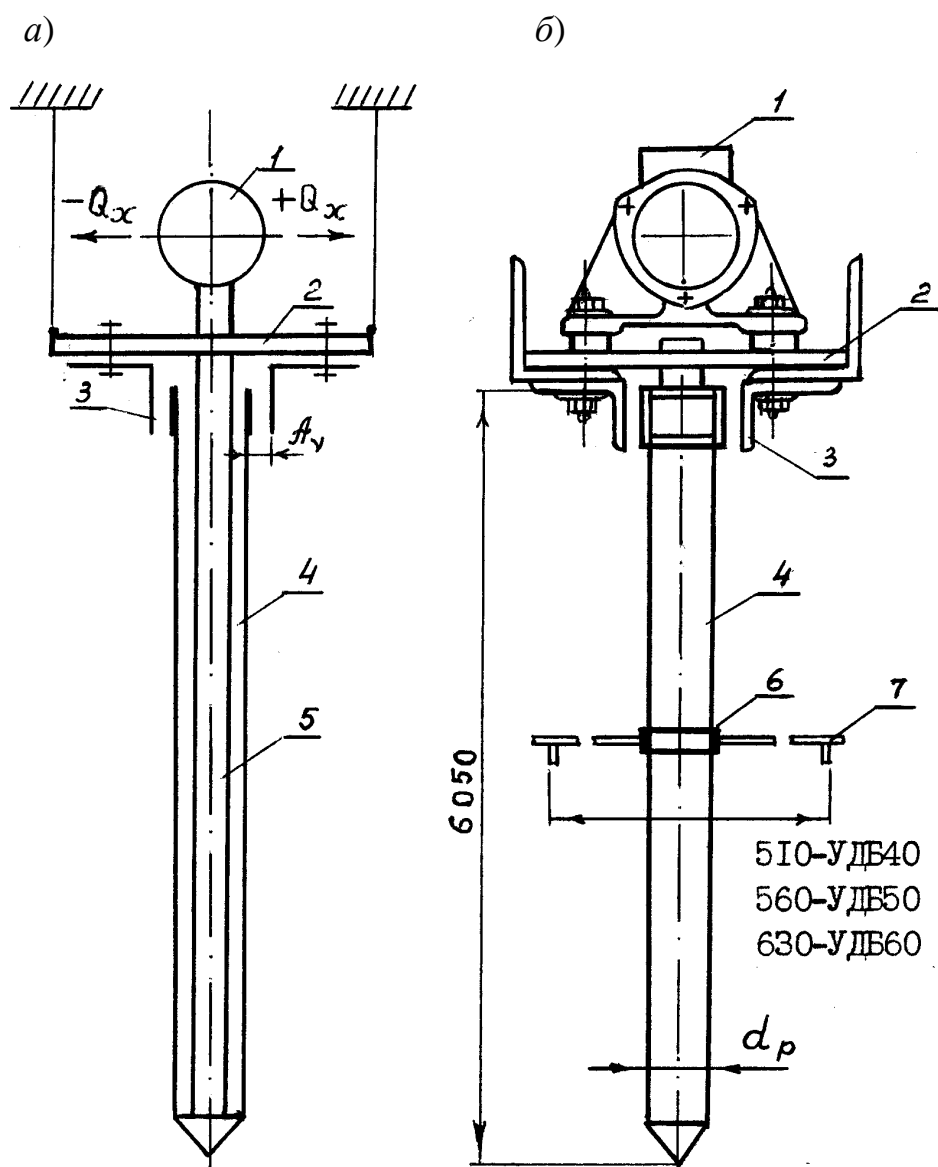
Виброимпульсный уплотнитель с цилиндрической рабочей частью ВГР2:
